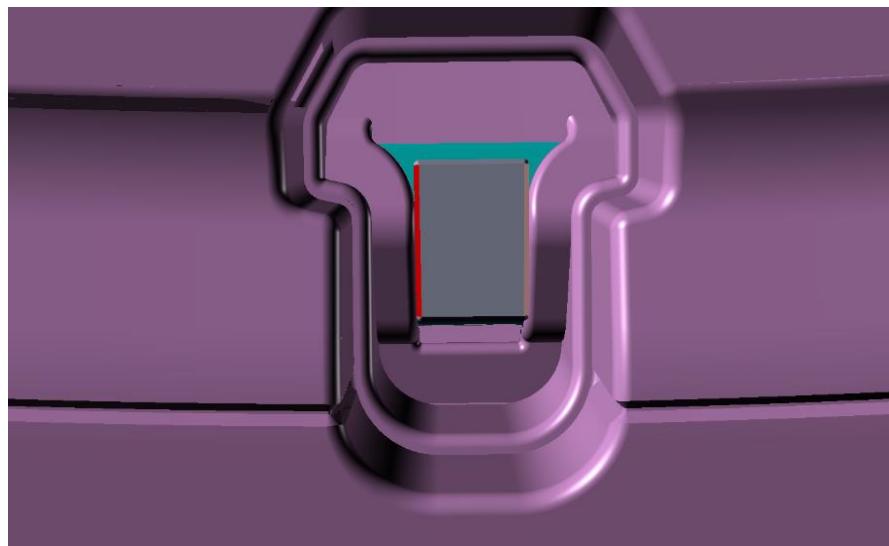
CAD Pieza del posicionador para RPS (Y-Z5)
